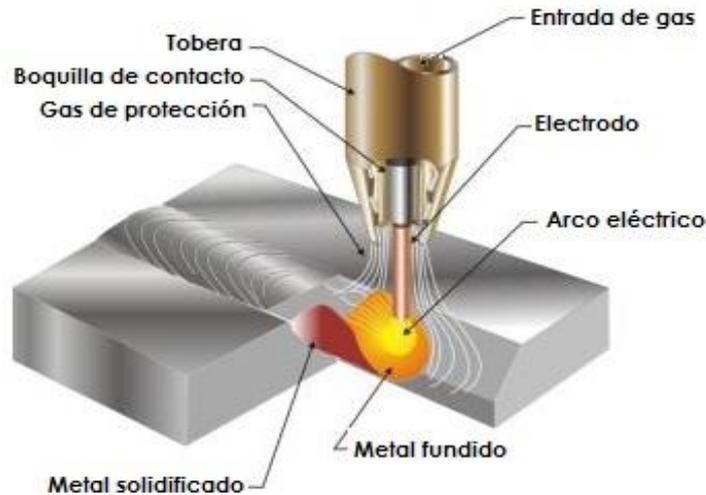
Esquema del proceso de soldadura GMAW.
